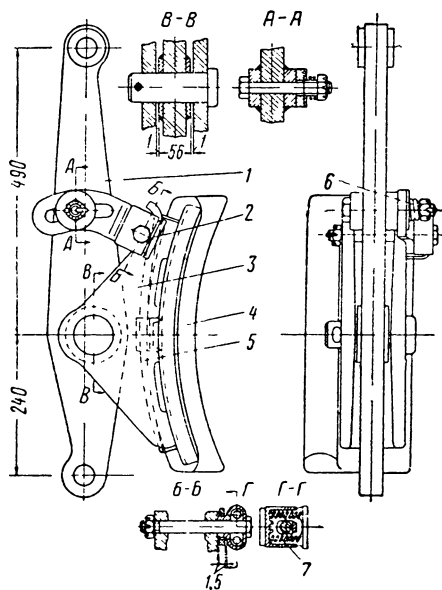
Крепление башмака с тормозной колодкой к подвеске:
